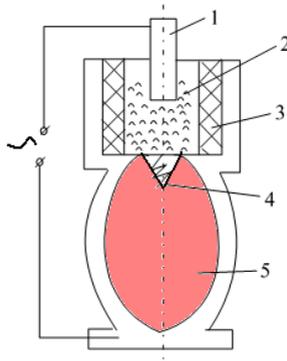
Схема процесса ЭШ подпитки слитков: 1 – электрод; 2 – шлак; 3 – формирующее кольцо; 4 – усадочная раковина; 5 – слиток
